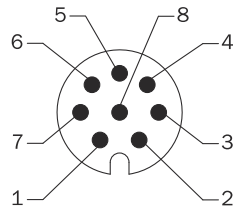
Ansicht Gerätestecker M12 am Encoder.
